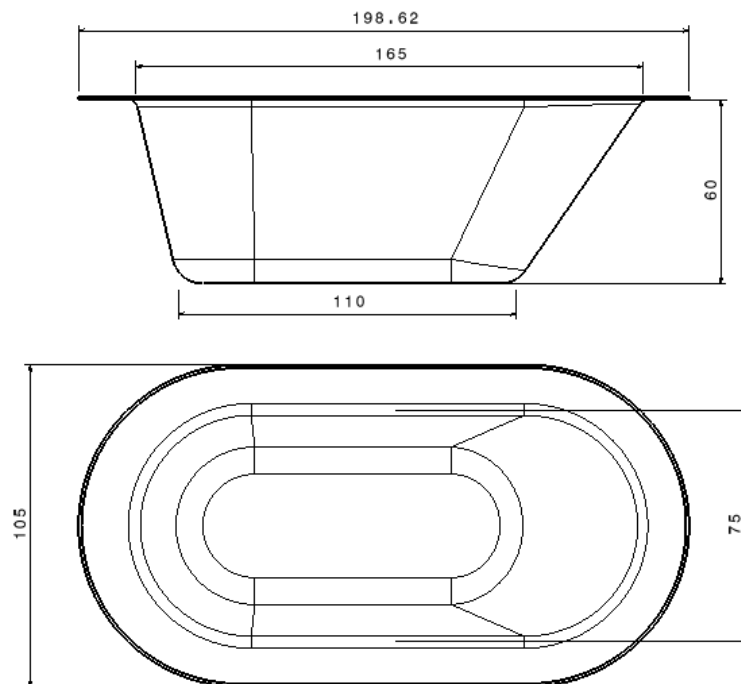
Cabina del dirigible, dimensiones principales. Cotas en mm
